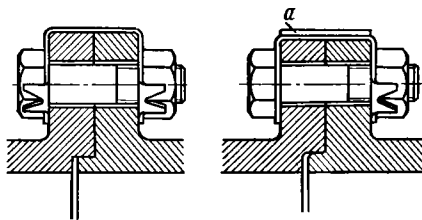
Скобы для стопорения гайки и болта, стягивающего фланцы
